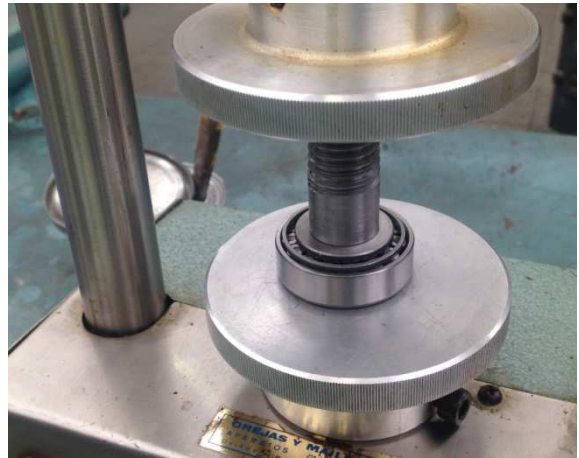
Cilindro con ajuste y rosca en rodamiento
